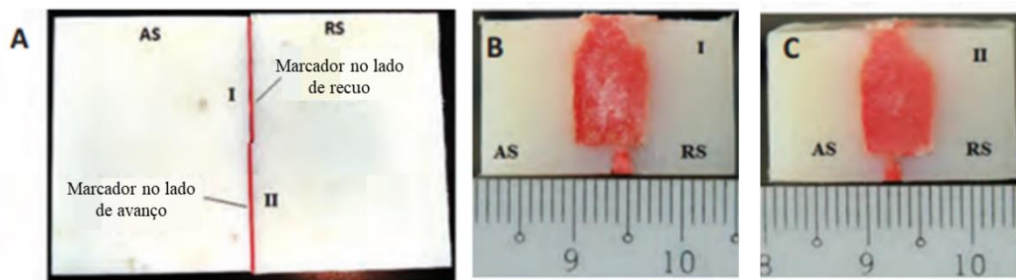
A - Amostras soldadas com marcador colocado paralelamente à direção de soldadura; B – Secção transversal da junta soldada da zona com marcador no LR; C - Secção transversal da junta soldada da zona com marcador no LA [19].
